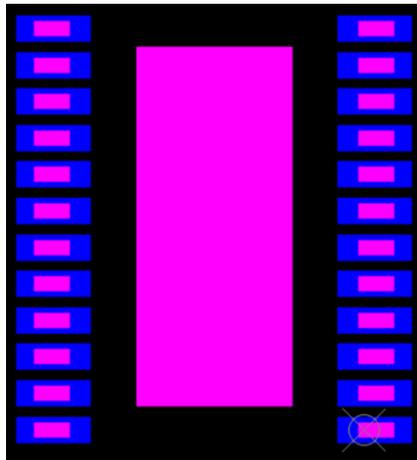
別の SO-24 PCB パッドに PWP0024T を取り付けられた場合、ピンク : TI PWP0024T リード、青 : その他の SO-24 PCB パッド
